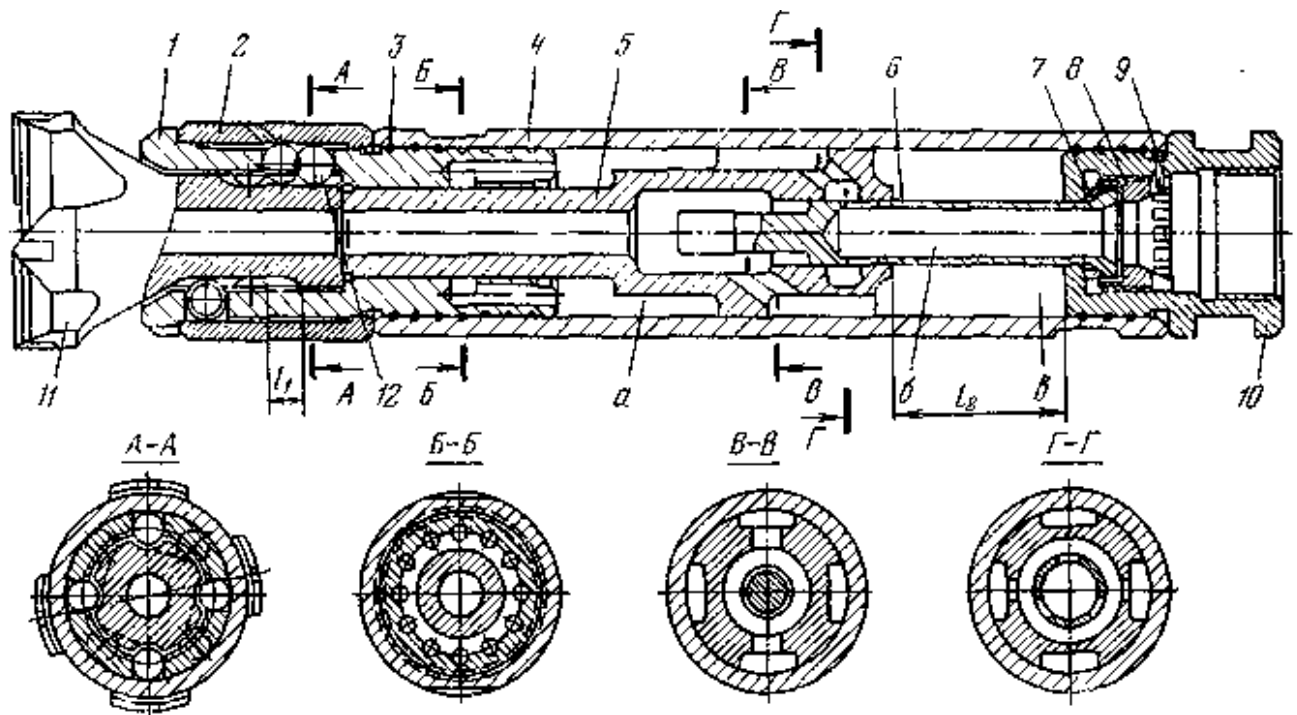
Занурюючий пневмоударник П-110: 1 — букса; 2 — кільце; 3 — пружина; 4 — циліндр; 5 - поршень-ударник; 6 — трубка розподільна; 7 — сідло; 8 — гайка регулювальна; 9 — стопор; 10 — перехідник; 11 — коронка; 12 — кульки
